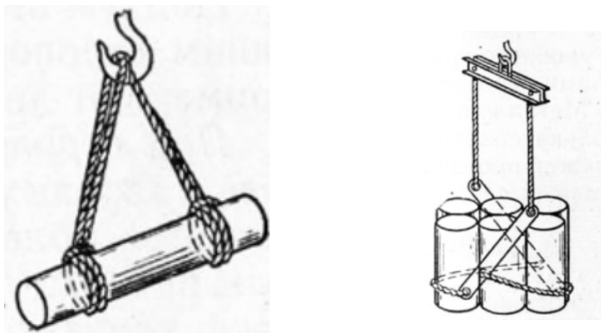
Конструкции грузозахватных устройств для транспортировки грузов
